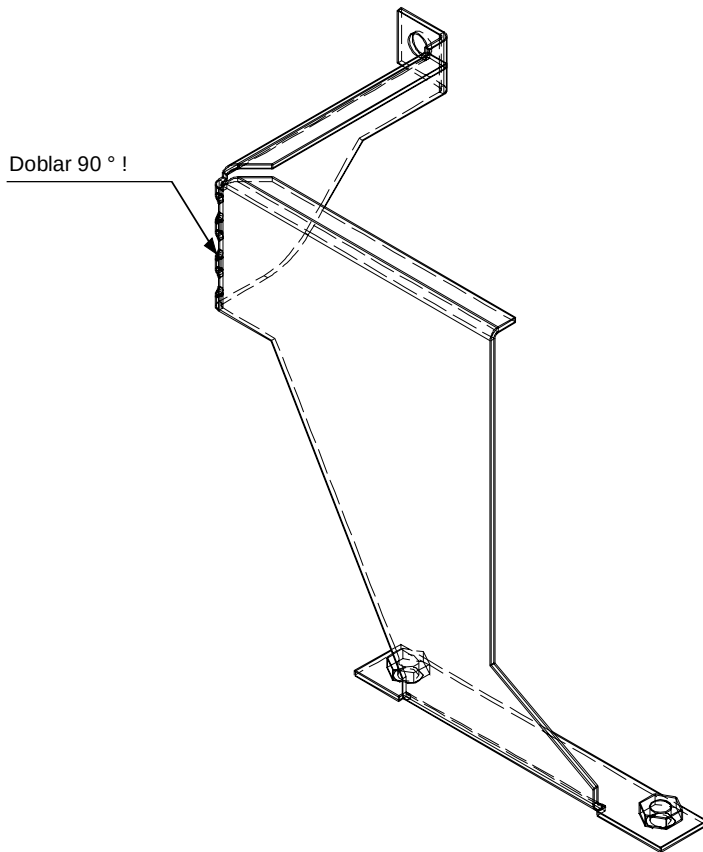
Estado final de la chapa de soporte para la tarjeta SSB
